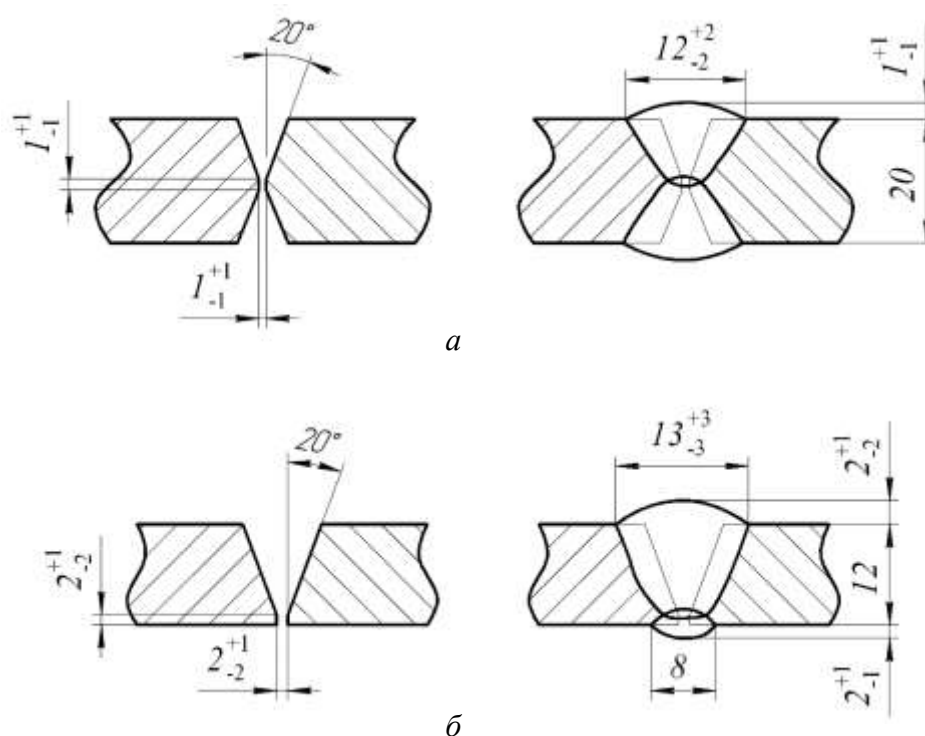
Конструктивные размеры подготовки кромок и тип сварного соединения стыковых швов пояса (а) и стенки (б)
